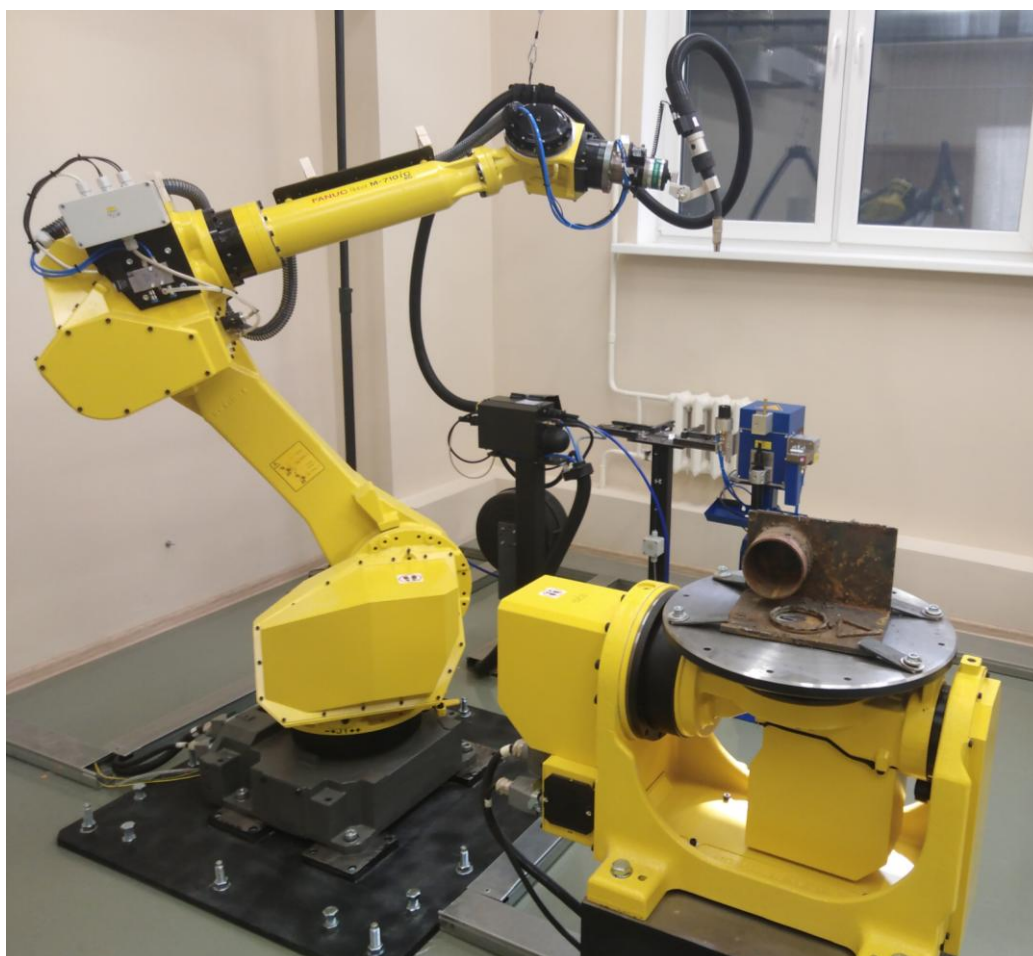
РТК дуговой сварки на базе робота FANUC M-710iC/50
